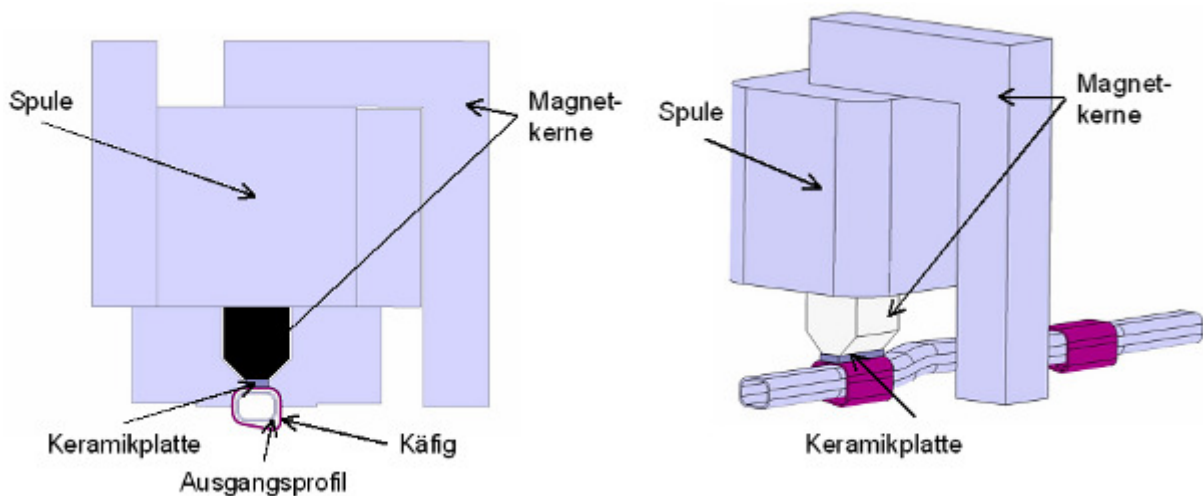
Konzipierung der Integration der lokalen magnetischen Bauteilerwärmung ins T-IHU-Werkzeug und konstruktive Ausführung
